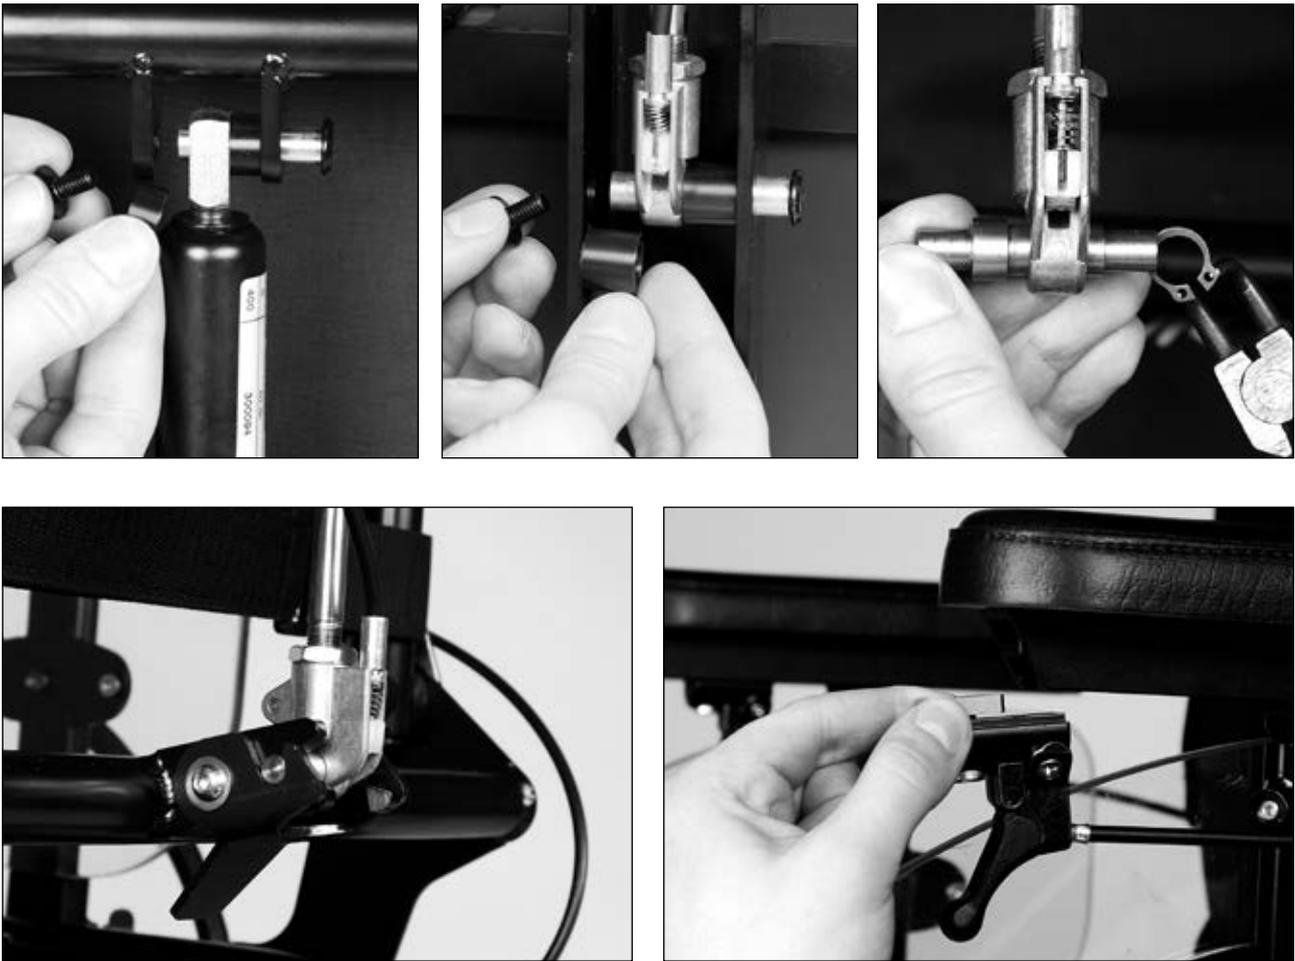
Reequipar o ajuste mecânico do ângulo de encosto
